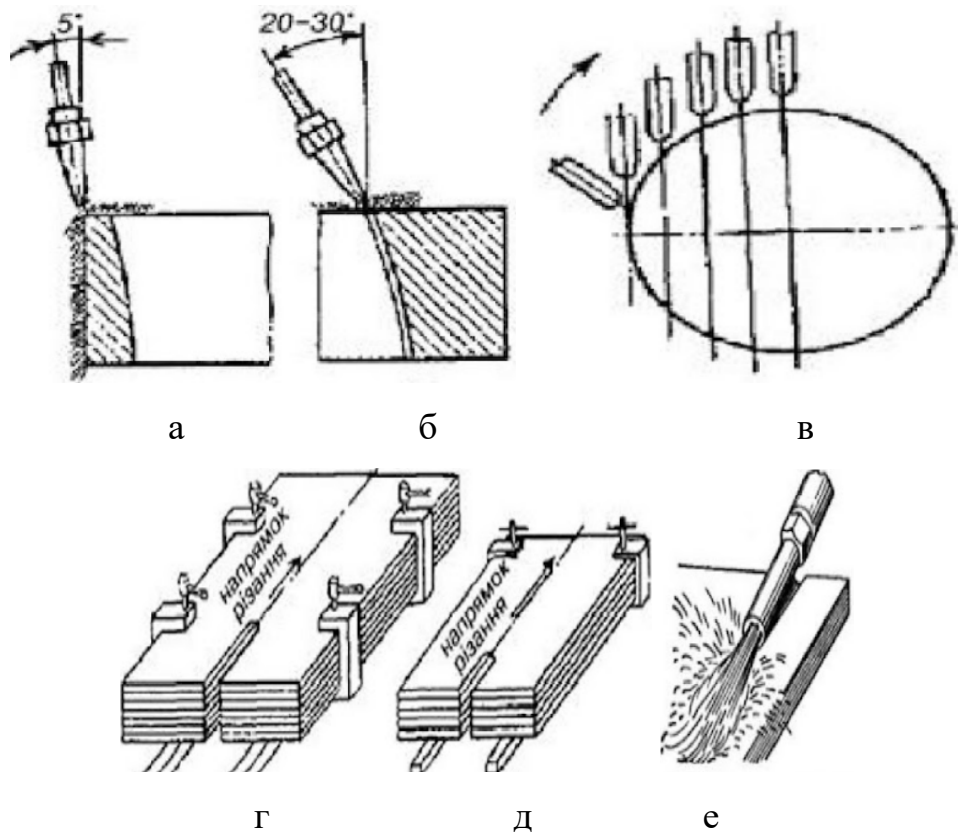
Розташування різача при різанні листового прокату на початку різання (а); у процесі різання (б); розташування різача при різанні круглих заготовок (в); пакетне різання листів сталі із щільним притисканням пакета (г); пакетне різання листів сталі із затисканням пакета зі сторони, протилежної початку різання (д), схема поверхневого кисневого різання (е)
